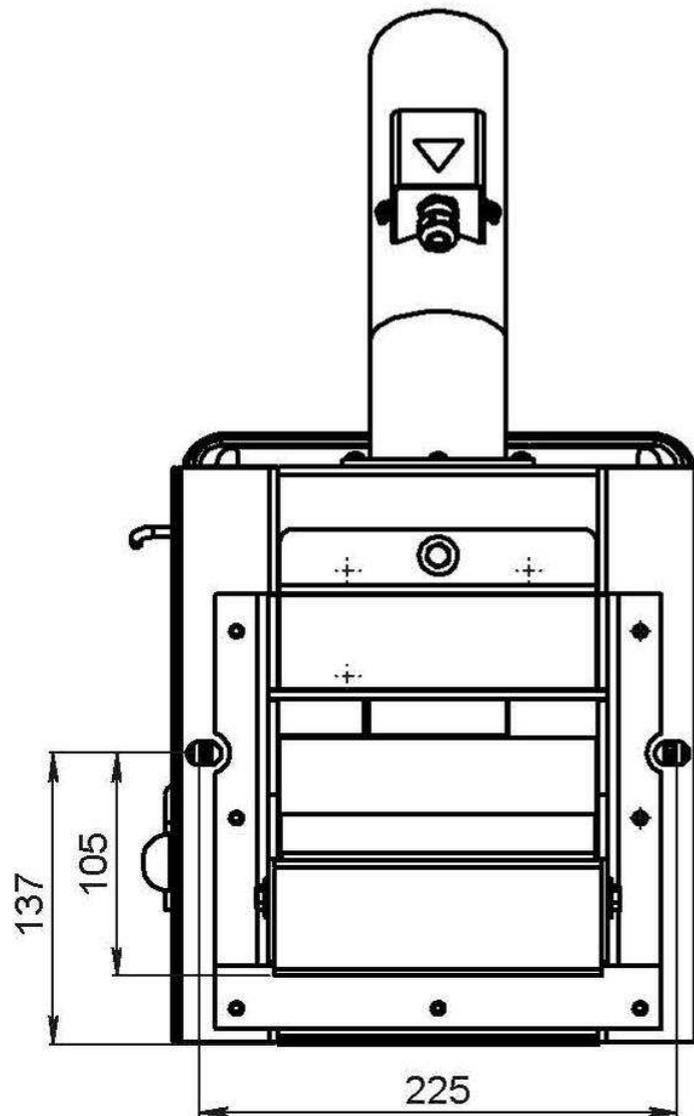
Dimensions de l'unité principale du brûleur GP IV – *vue de face.
